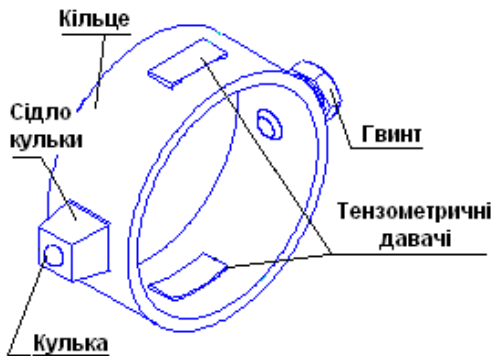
Принципова схема конструкції давача для вимірювання осьової сили притискування долота до вибою свердловини
